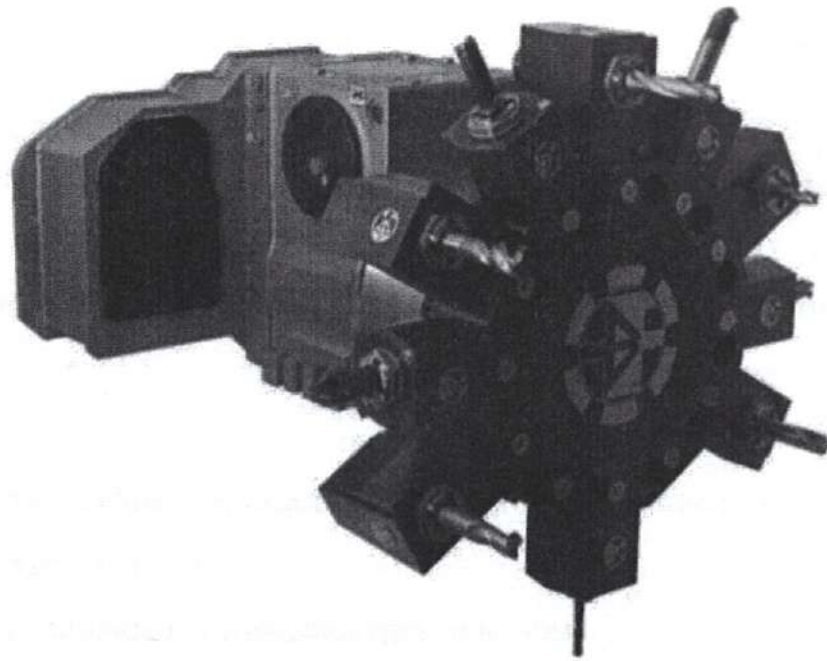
Револьверна головка токарних верстатів з одним приводом для повороту інструментального диска та осьового інструмента типу TBMR 160.
